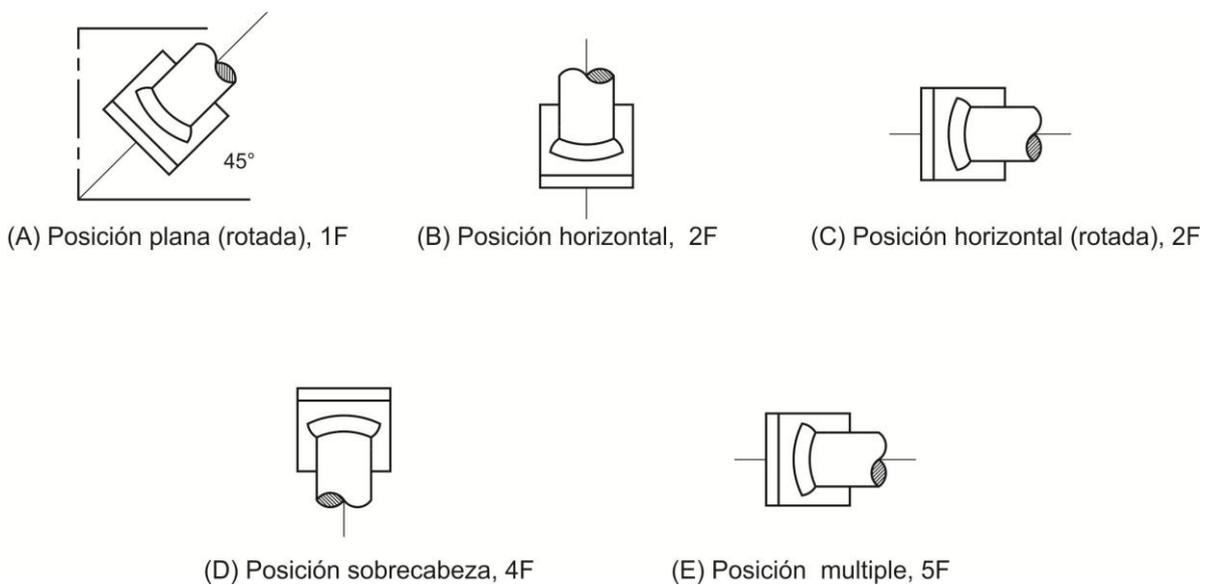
Posiciones para las soldaduras de filete.
